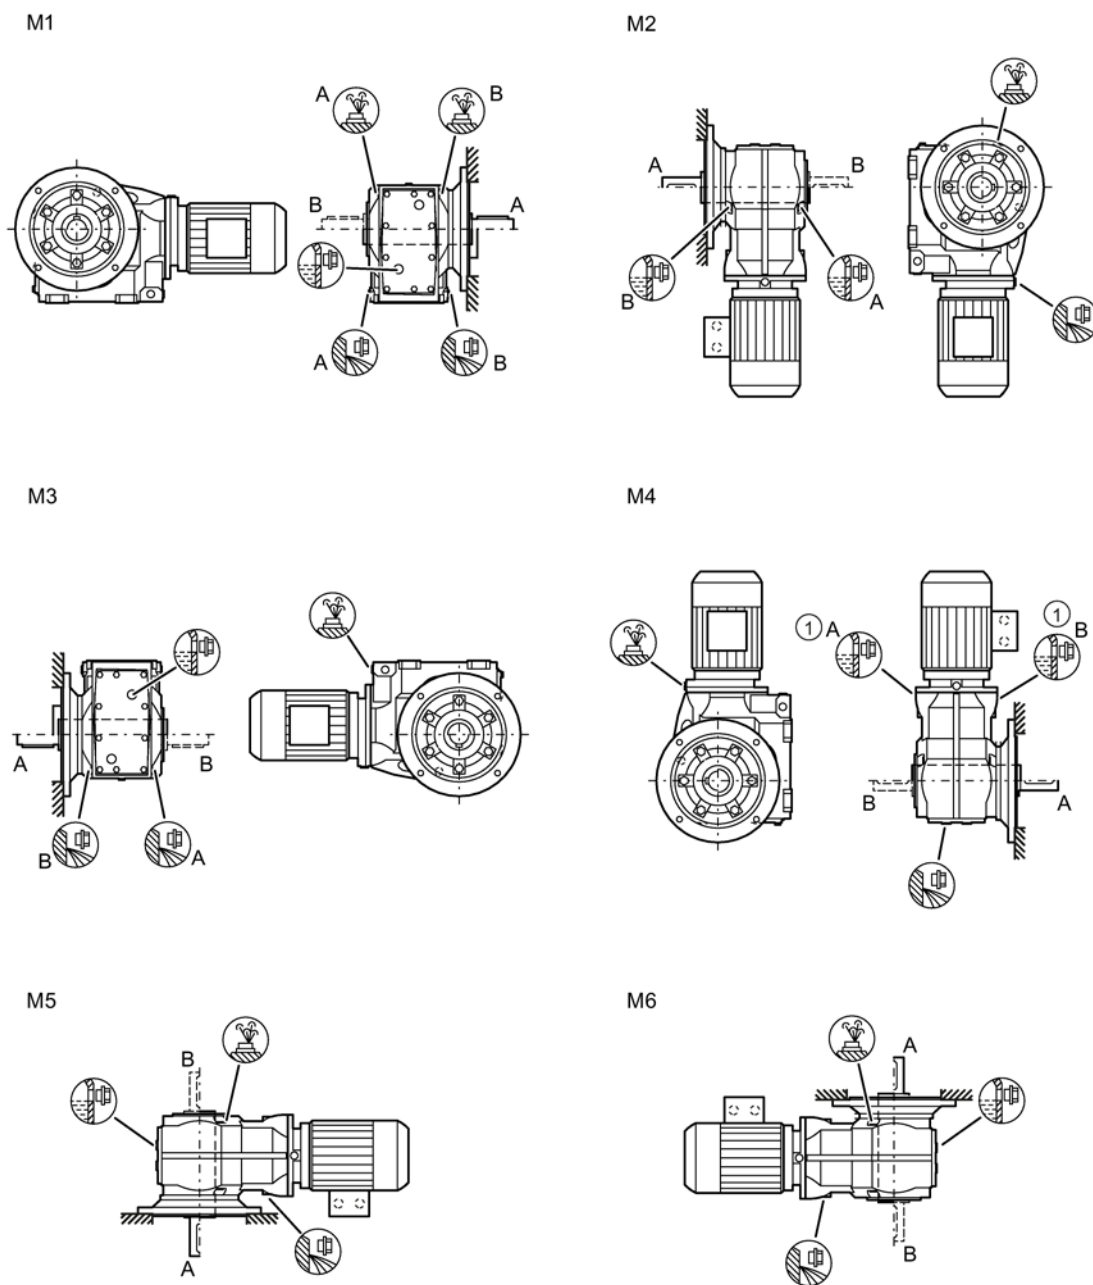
Монтажные положения для конического редуктора К.Ф в исполнении с фланцем и KAZ с фланцем корпуса, типоразмеры 39-189
